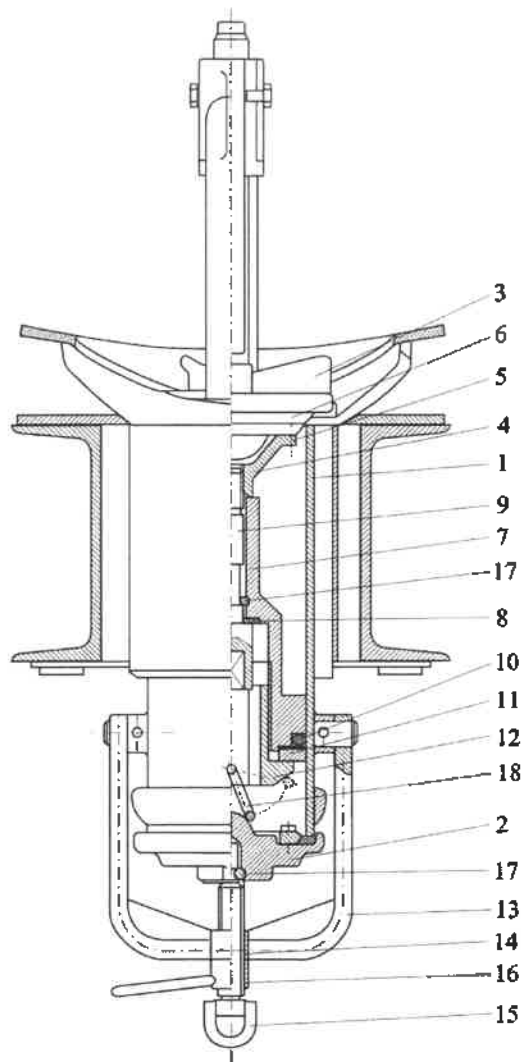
Конструкция сливного прибора с тройной защитой [7]
